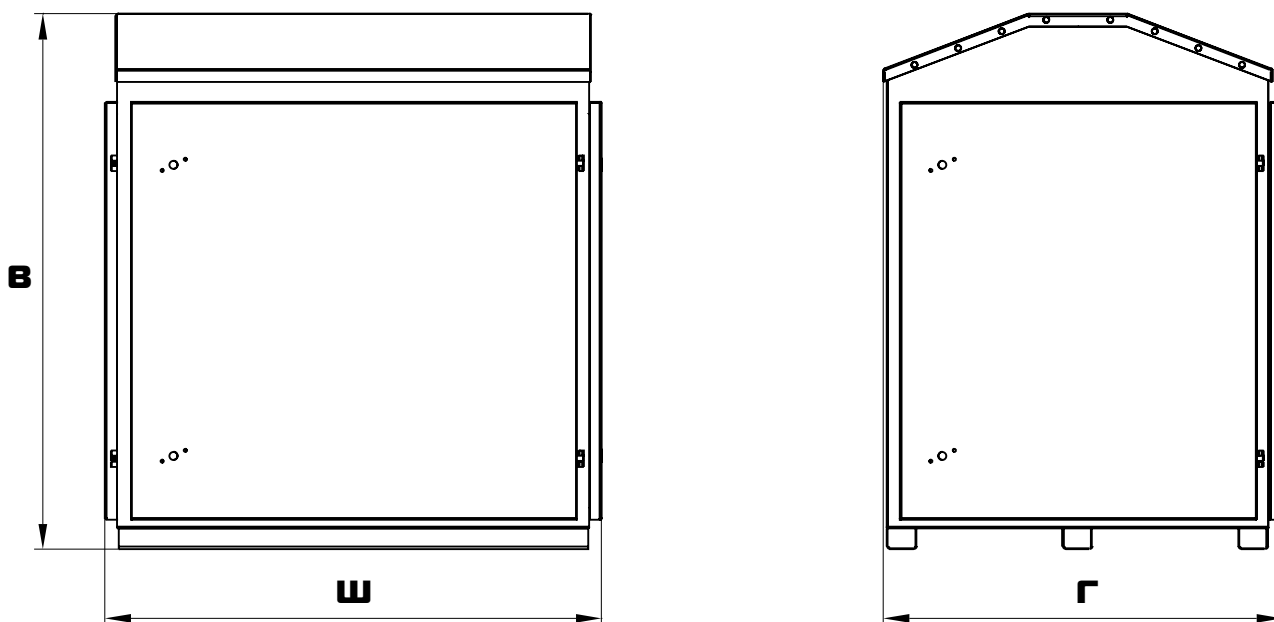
Габаритный чертеж СТС-5-С IP54 25-100 кВА
